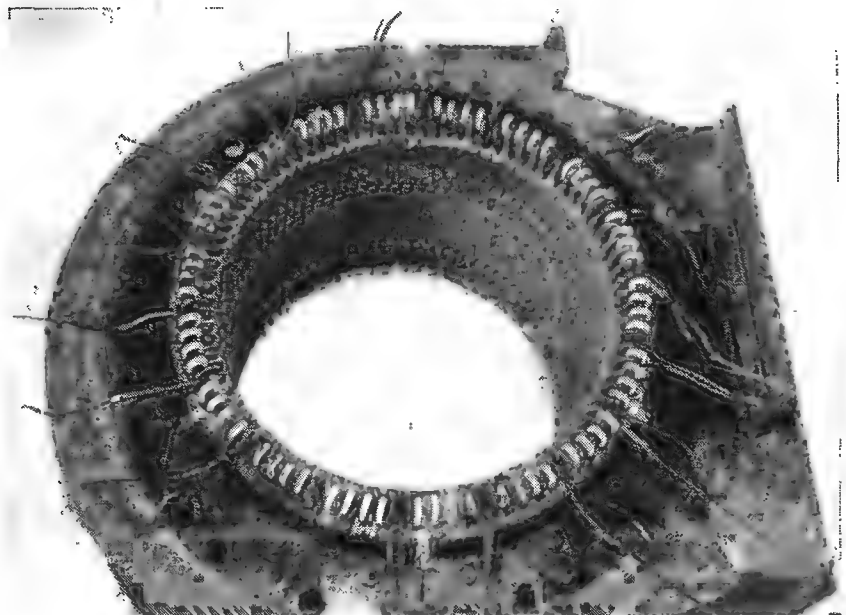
Двухслойная обмотка альтернатора 1400 ква, 6,3 кв, 1000/1800 об/мин в стадии изготовления (ЧКД — Прага, н. п.).
